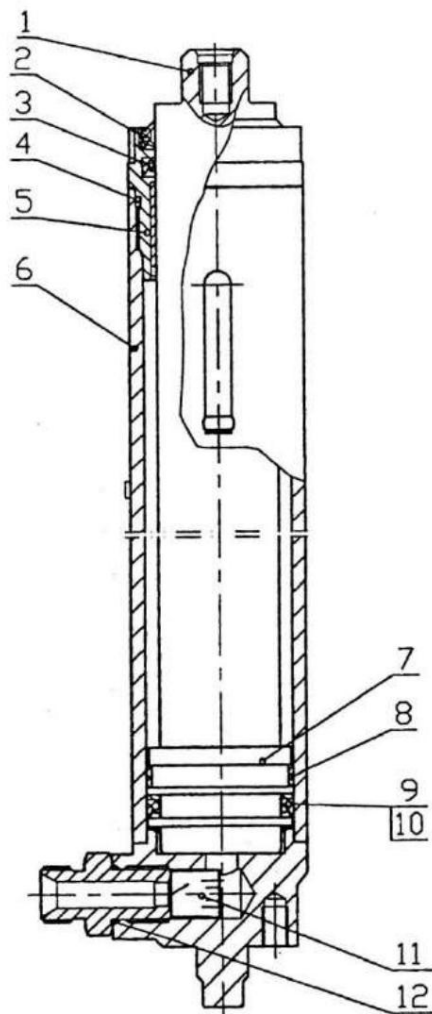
Elevación y descenso del cilindro (Figura 10-1, 10-4)
